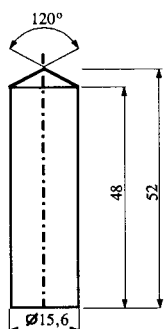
Цилиндрический бронзовый поршень; размеры в мм
